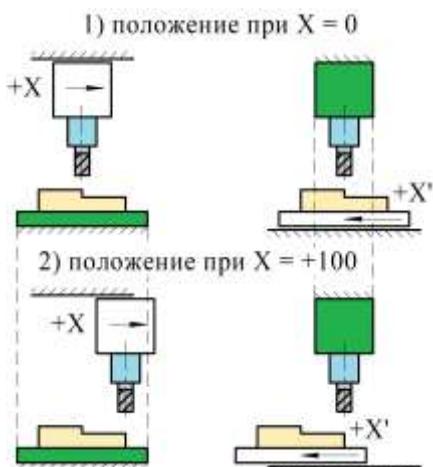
Положение инструмента относительно заготовки, при перемещении РО с инструментом или РО с заготовкой
